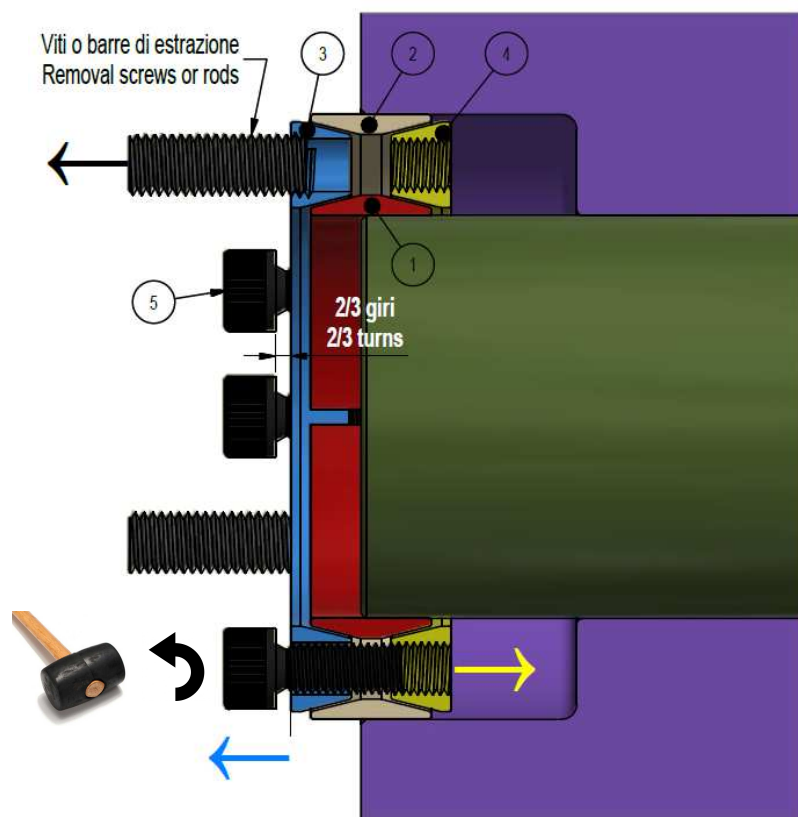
Sbloccaggio degli anelli di spinta e rimozione del calettatore.
